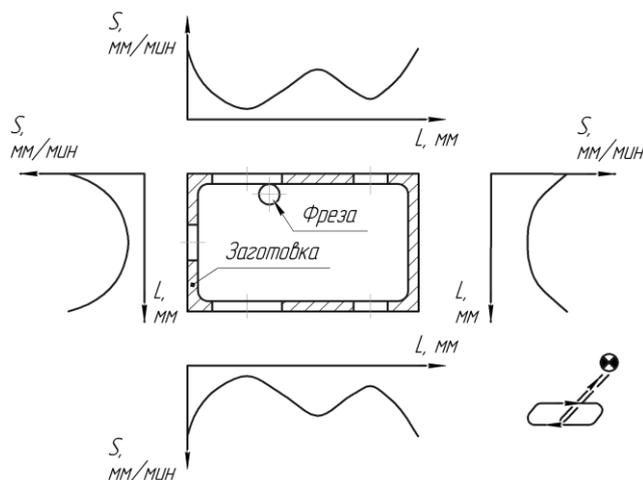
Способ управления показателями точности фрезерования нежесткой детали
